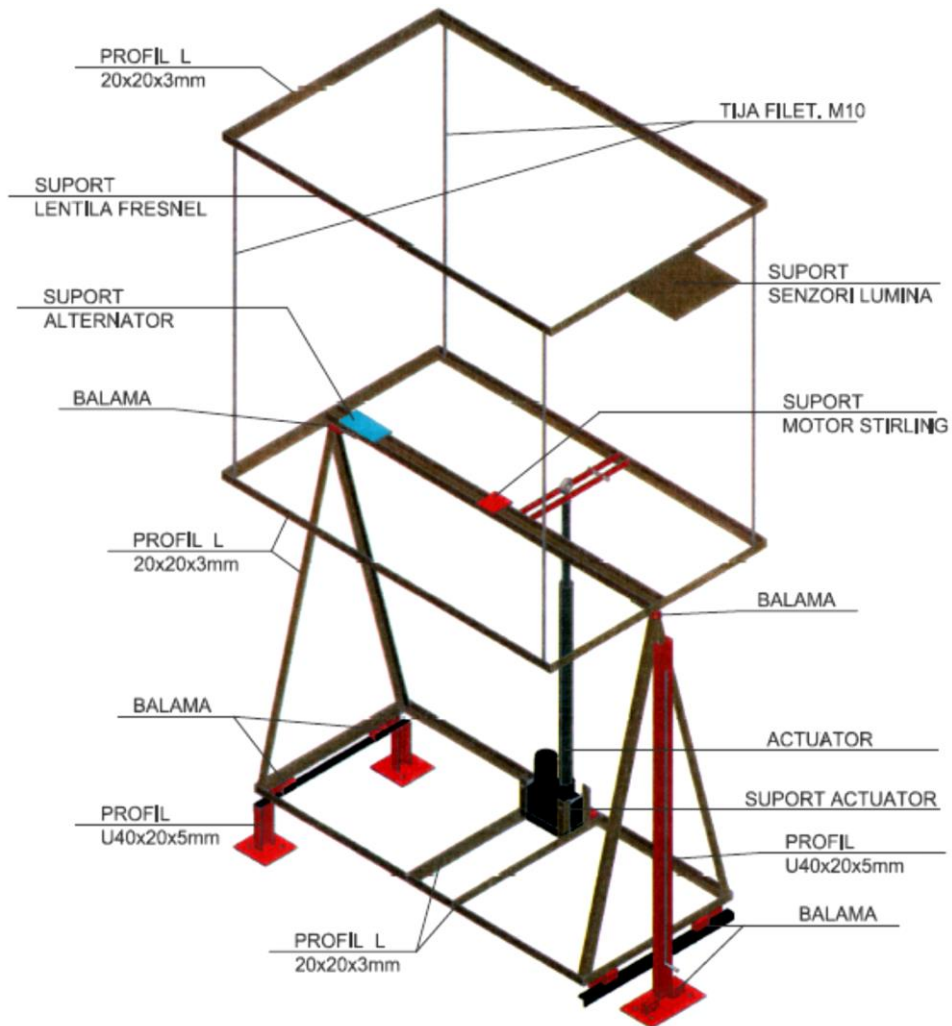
Instalație experimentală prototip 2 - cadru suport vedere izometrică
